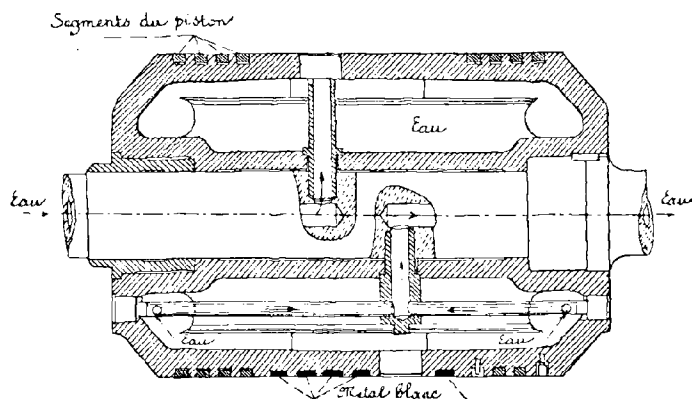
Piston de la machine Kœrting, avec circulation d'eau et garniture de métal blanc.
